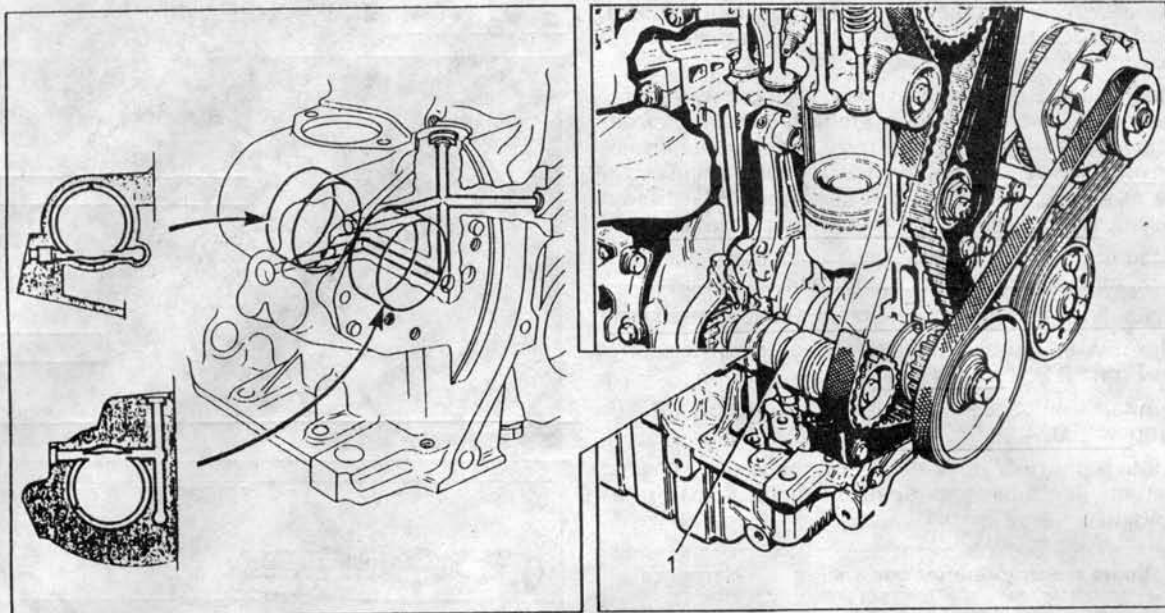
Промежуточный вал (1) привода масляного насоса – двигатель V172
